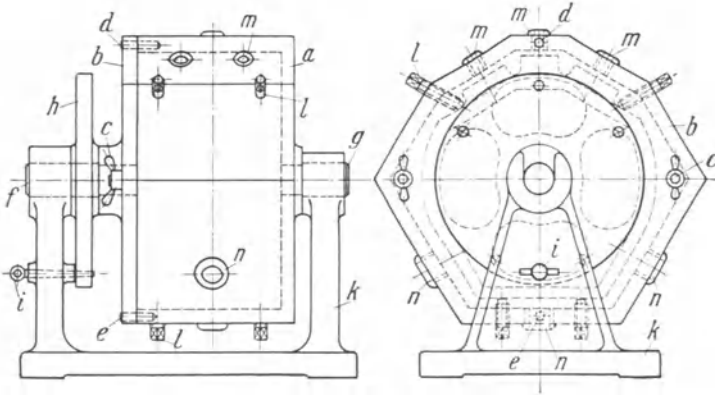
Drehbarer Bohrkasten für schwere Arbeitsstücke.
